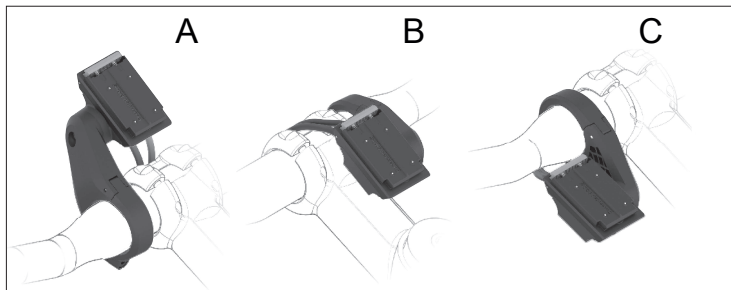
Posiciones de montaje del soporte para ordenador de control
